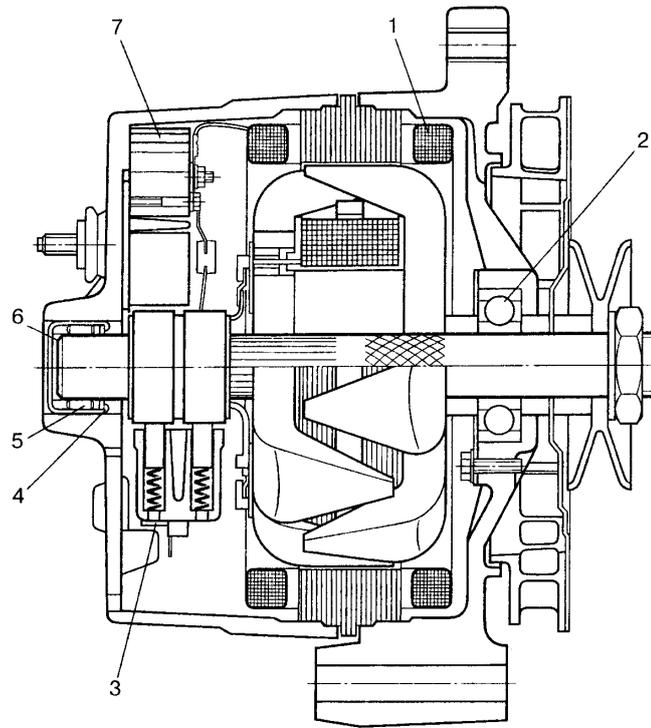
Устройство генератора 12SI - 100 фирмы Deico Remy: 1 - статор; 2 - шарикоподшипник; 3 - щеткодержатель; 4 - уплотнение подшипника; 5 - роликовый (игольчатый) подшипник; 6 - полость для смазки подшипника; 7 - выпрямительный блок
